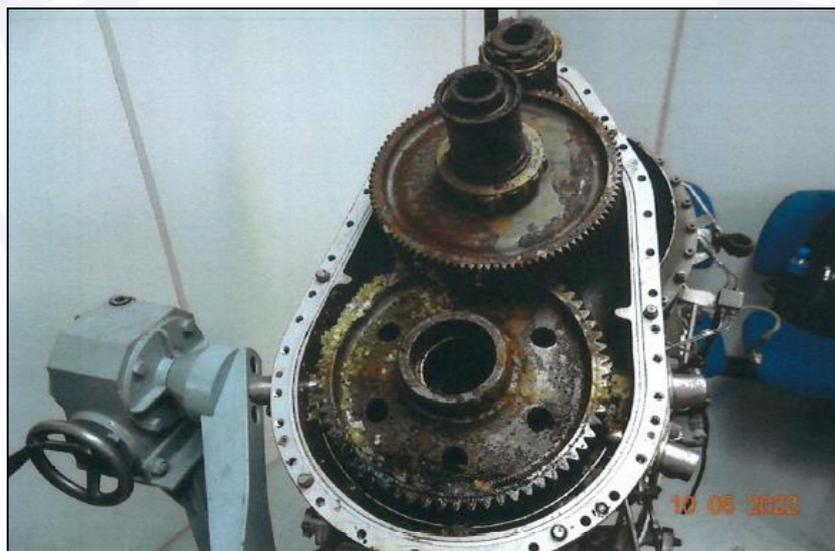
Vista geral das engrenagens de redução do módulo 05 do motor SN 42326TEC.
